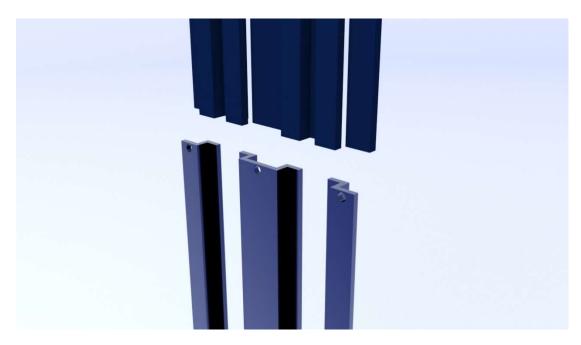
Render detalle montaje guía sobre soporte mesa
